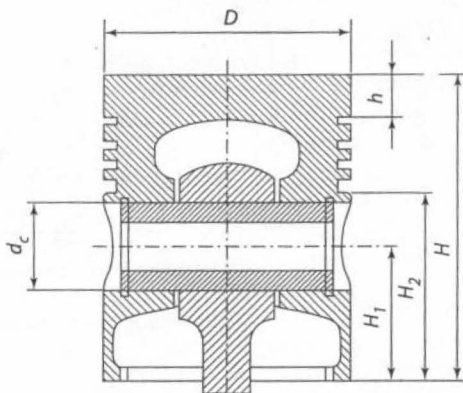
Esquema de dimensiones básicas de diseño del pistón.
